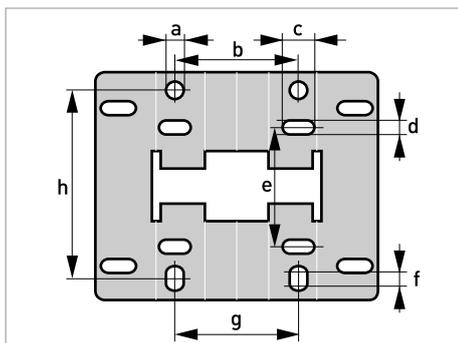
Dimensiones de la placa de montaje del alojamiento en pared
